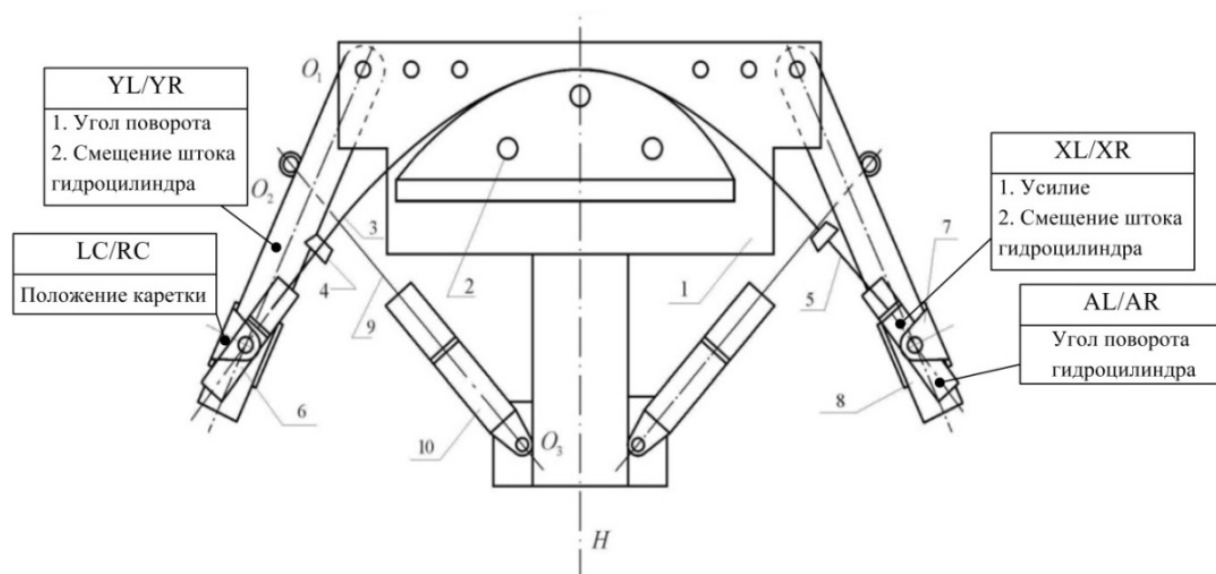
Схема гибочно-растяжного пресса с ЧПУ: 1 – неподвижный стол; 2 – формообразующая оправка; 3 – заготовка; 4 – зажимные патроны; 5 – шток растяжного гидроцилиндра; 6 – растяжной гидроцилиндр; 7 – каретка; 8 – гибочный рычаг; 9 – шток гибочного гидроцилиндра; 10 – гибочный гидроцилиндр; O_1 – ось поворота гибочного рычага; O_2 – ось вращения гибочного гидроцилиндра на гибочном рычаге; O_3 – ось вращения гибочного гидроцилиндра на станине пресса; Н-Н – ось симметрии станка; YL/YR; LC/RC; XL/RL; AL/AR – программируемые параметры пресса
